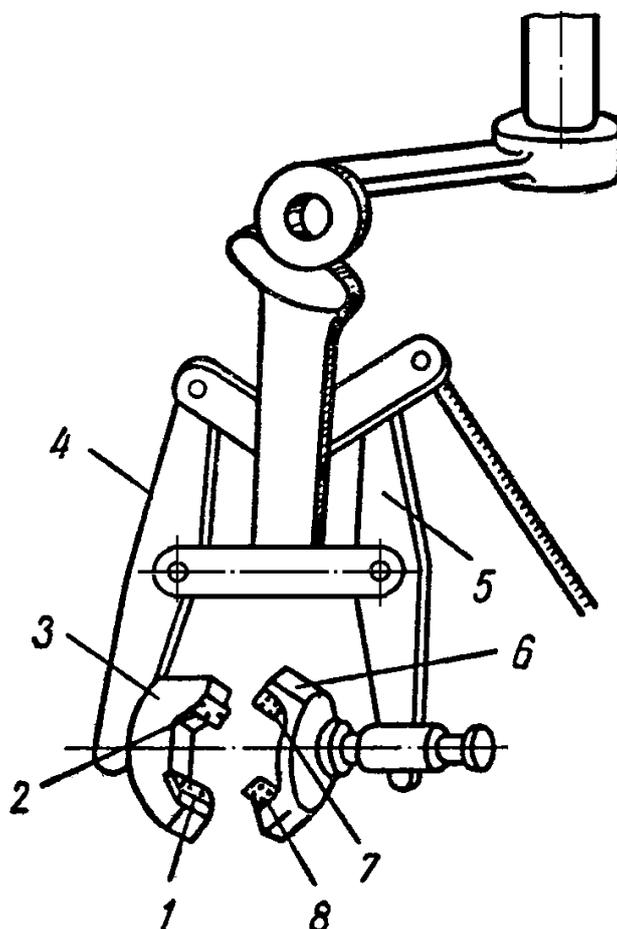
Схема конструкции хонинговального устройства для обработки шеек вала: 1, 2, 7, 8 – абразивные бруски; 3, 6 – колодки; 4, 5 – разжимные скобы
